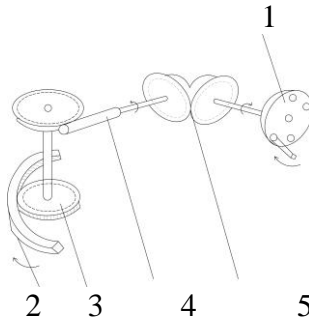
Схема секторного механізму з внутрішнім зчепленням корінної шестерні:
